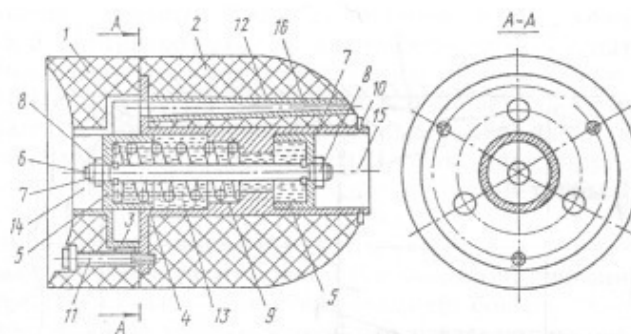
Очистное устройство для разжижения и перемещения парафиновых пробок, где 1, 2 – части пустотелого корпуса; 3, 4 – направляющие; 5 – поршень; 6 – шток; 7 – стопорные кольца; 8 – гайка; 9 – пружина; 10 – стопорное кольцо; 11 – болты; 12 – конусообразные кольца (3 шт.); 13 – полость.
